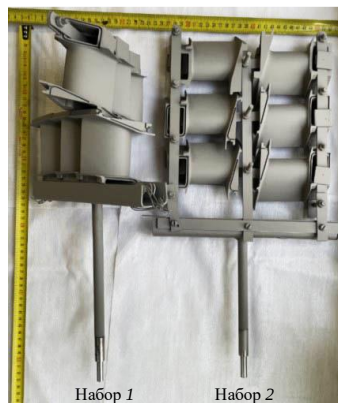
Внешний вид имитаторов крупногабаритных деталей газотурбинного двигателя и образцов-свидетелей после нанесения покрытия
